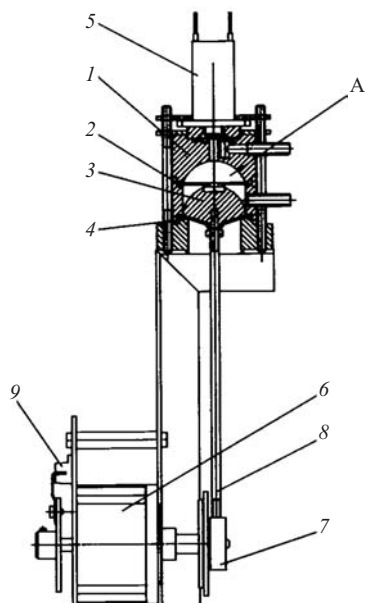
1 — корпус дозатора, 2 — упругая дозировочная диафрагма, 3 — торцевая часть плунжера, 4 — упругая дополнительная диафрагма, 5 — выходной клапан, 6 — шаговый двигатель, 7 — эксцентриситет с подшипником, 8 — плунжер, 9 — оптический датчик, А — камера вытеснения.
